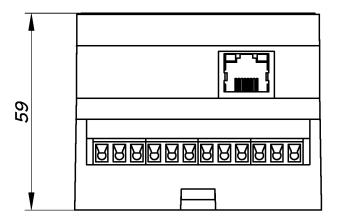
Габаритные размеры контроллера в корпусе исполнения -DIN
